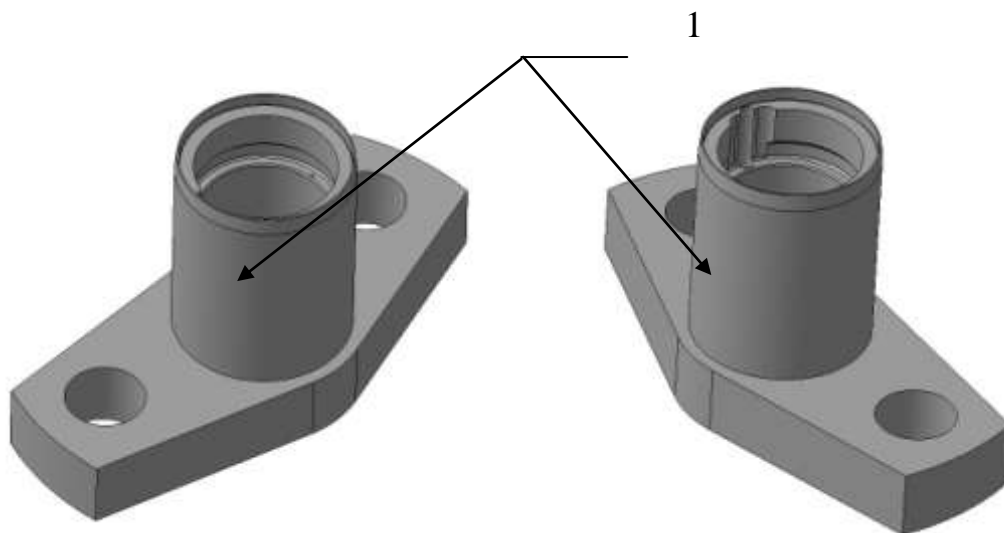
Корпус (1 – поверхность для захвата промышленным роботом)
